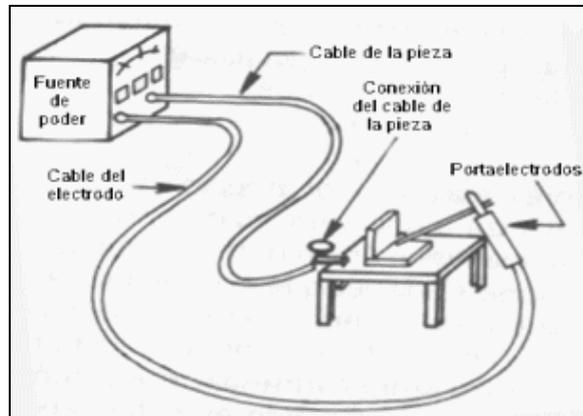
Soldadura por arco eléctrico³¹.
